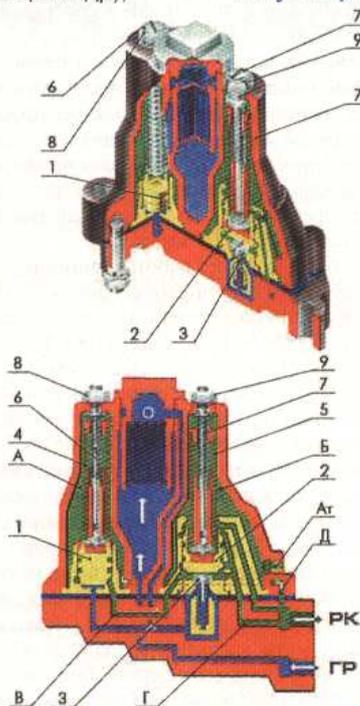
Регулятор давления ЗРД: 1 — выключющий клапан; 2 — включающий клапан; 3 — обратный клапан; 4, 5 — пружина; 6, 7 — стержень; 8, 9 — гайка; АТ — атмосфера; РК — разгрузочные клапаны; ГР — главные резервуары; А, Б — полости; В, Г, Д — каналы
